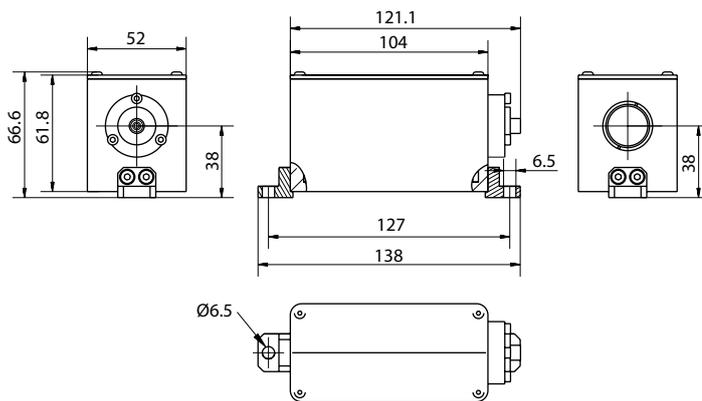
Габаритные размеры коллиматора с изолятором лазера модели FFS200CH1.
